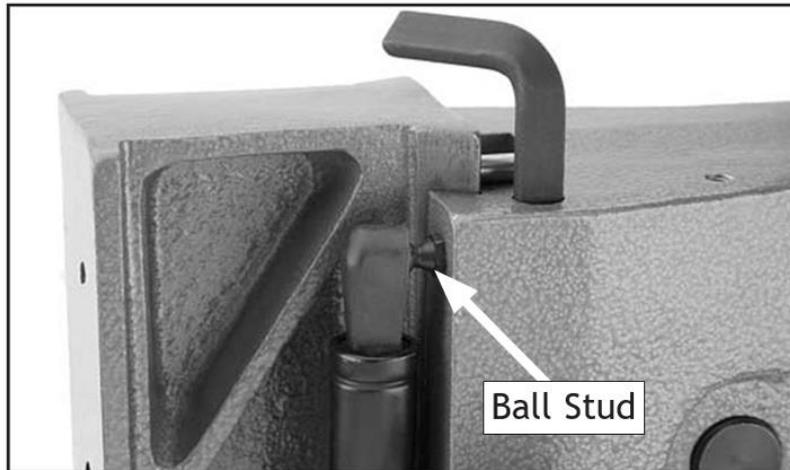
Крепление газлифта к корпусу сверлильного станка.
